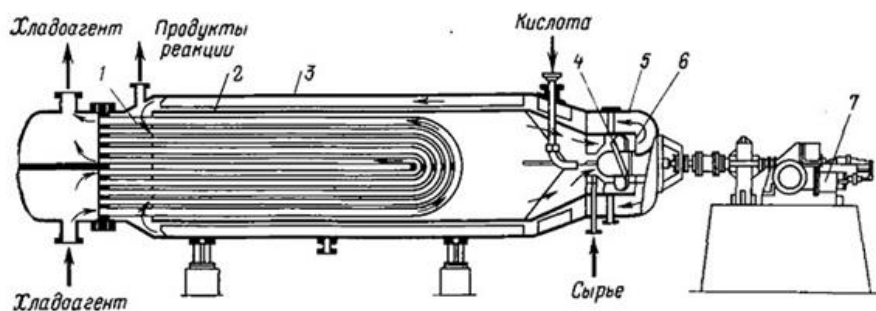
Горизонтальный реактор сернокислотного алкилирования: 1 – трубчатка; 2, 5 – циркуляционная труба; 3 – корпус; 4 – перемещающее устройство; 6 – направляющие лопасти; 7 – привод [27]
